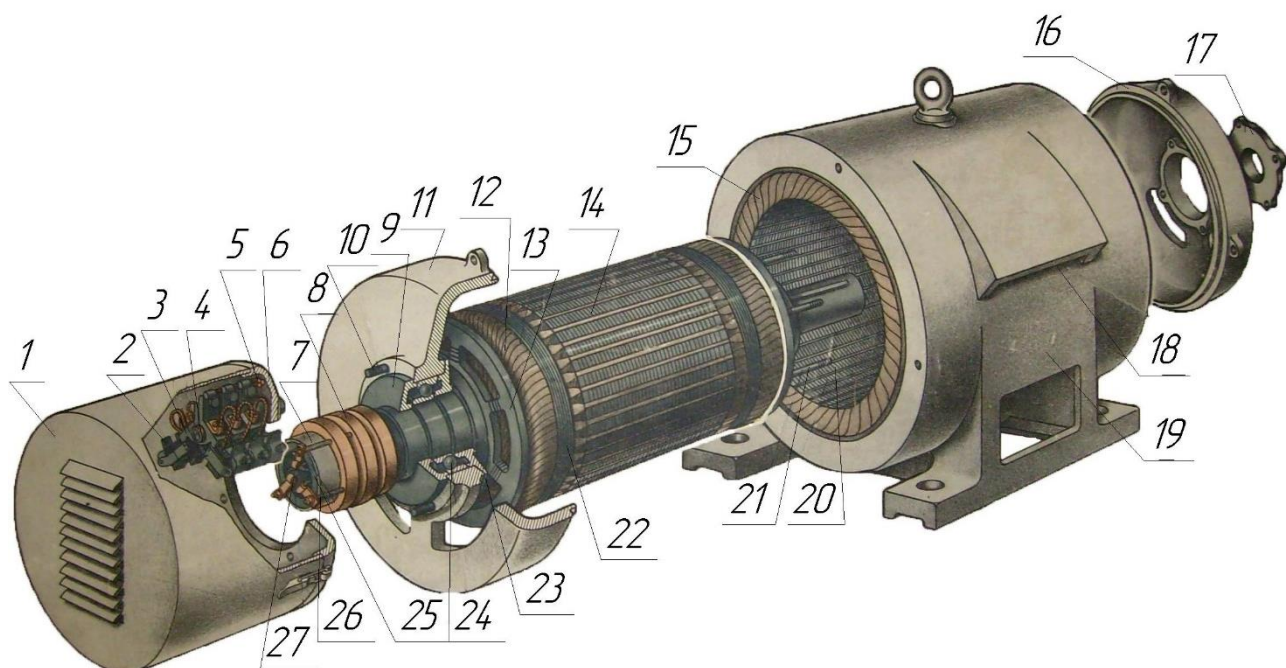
Трехфазный асинхронный двигатель с фазным ротором
